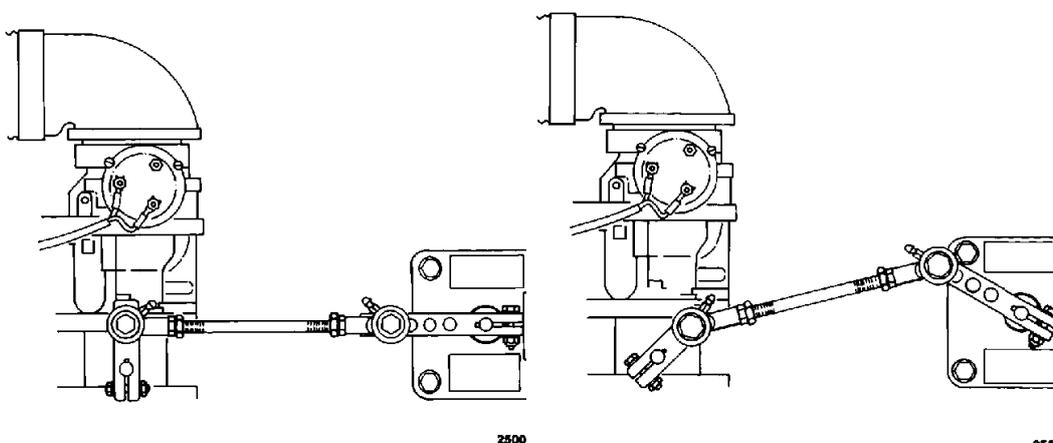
Tringlerie de compensation du carburateur à combustible minimum
